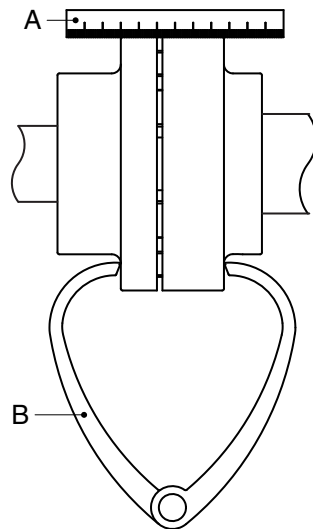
Aligning the coupling by means of a ruler and a pair of outside calipers.
